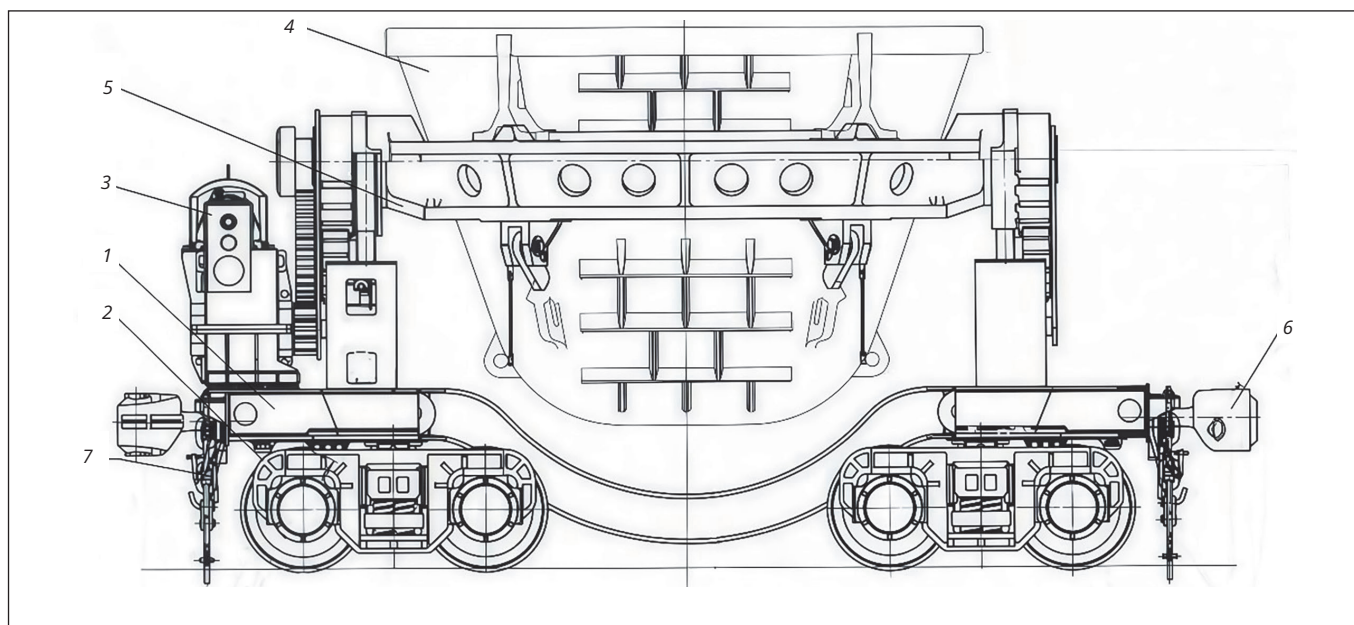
Шляковоз 16,5 СП: 1 – рама; 2 – тележка ходовая; 3 – механизм кантования; 4 – шлаковая чаша; 5 – опорное кольцо; 6 – автосцепное устройство; 7 – захват рельсовый
